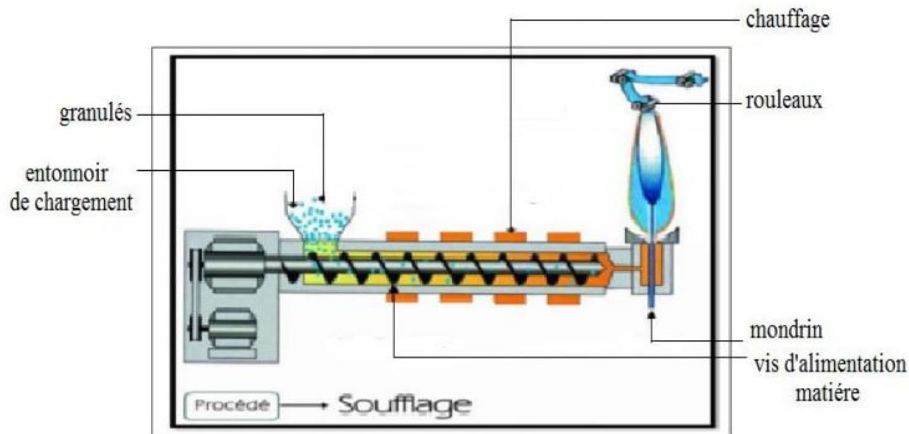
Représentative de la machine d'extrusion-soufflage [32].
